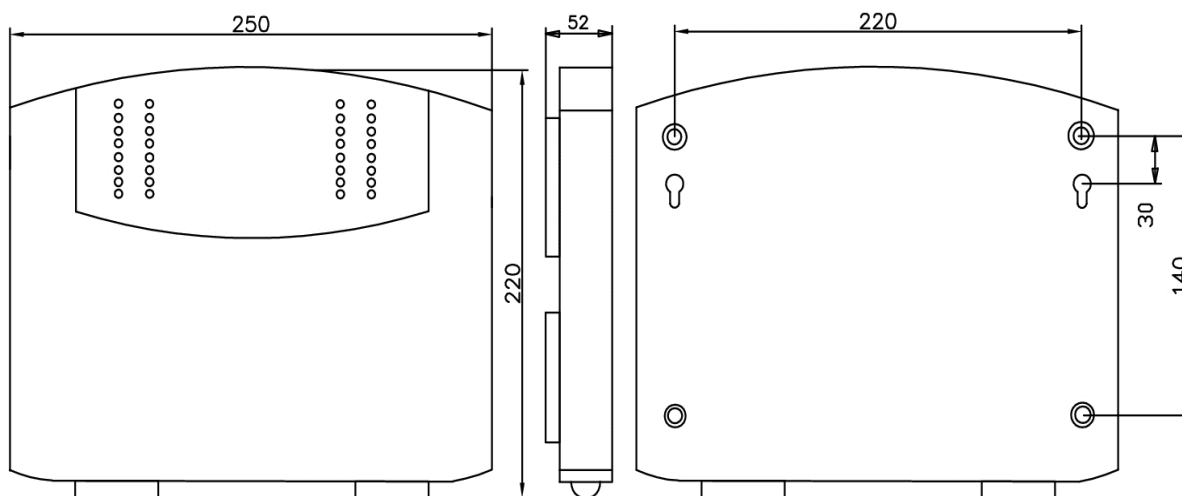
Габаритные и установочные размеры прибора, пластмассовый корпус
